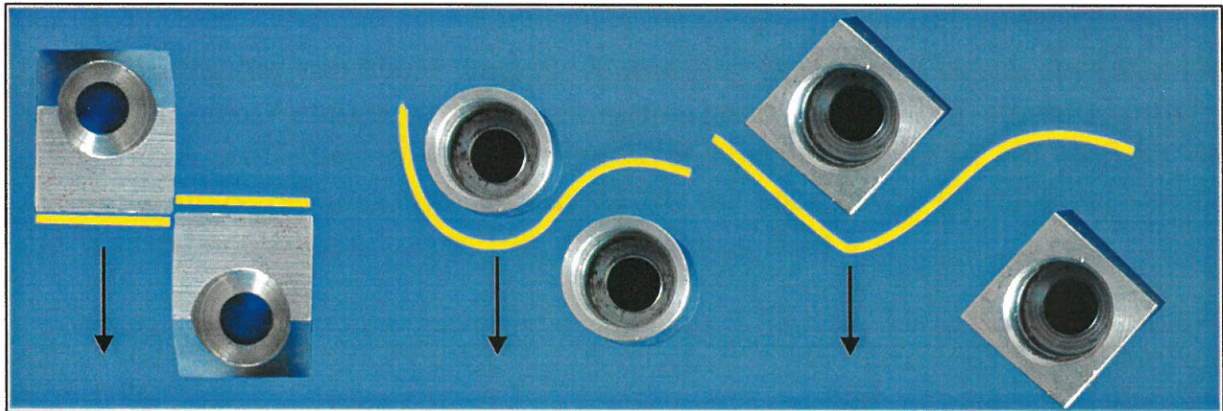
Zerkleinerungswerkzeuge als Schneide und Gegenschneide einer halbtechnischen Versuchseinrichtung
